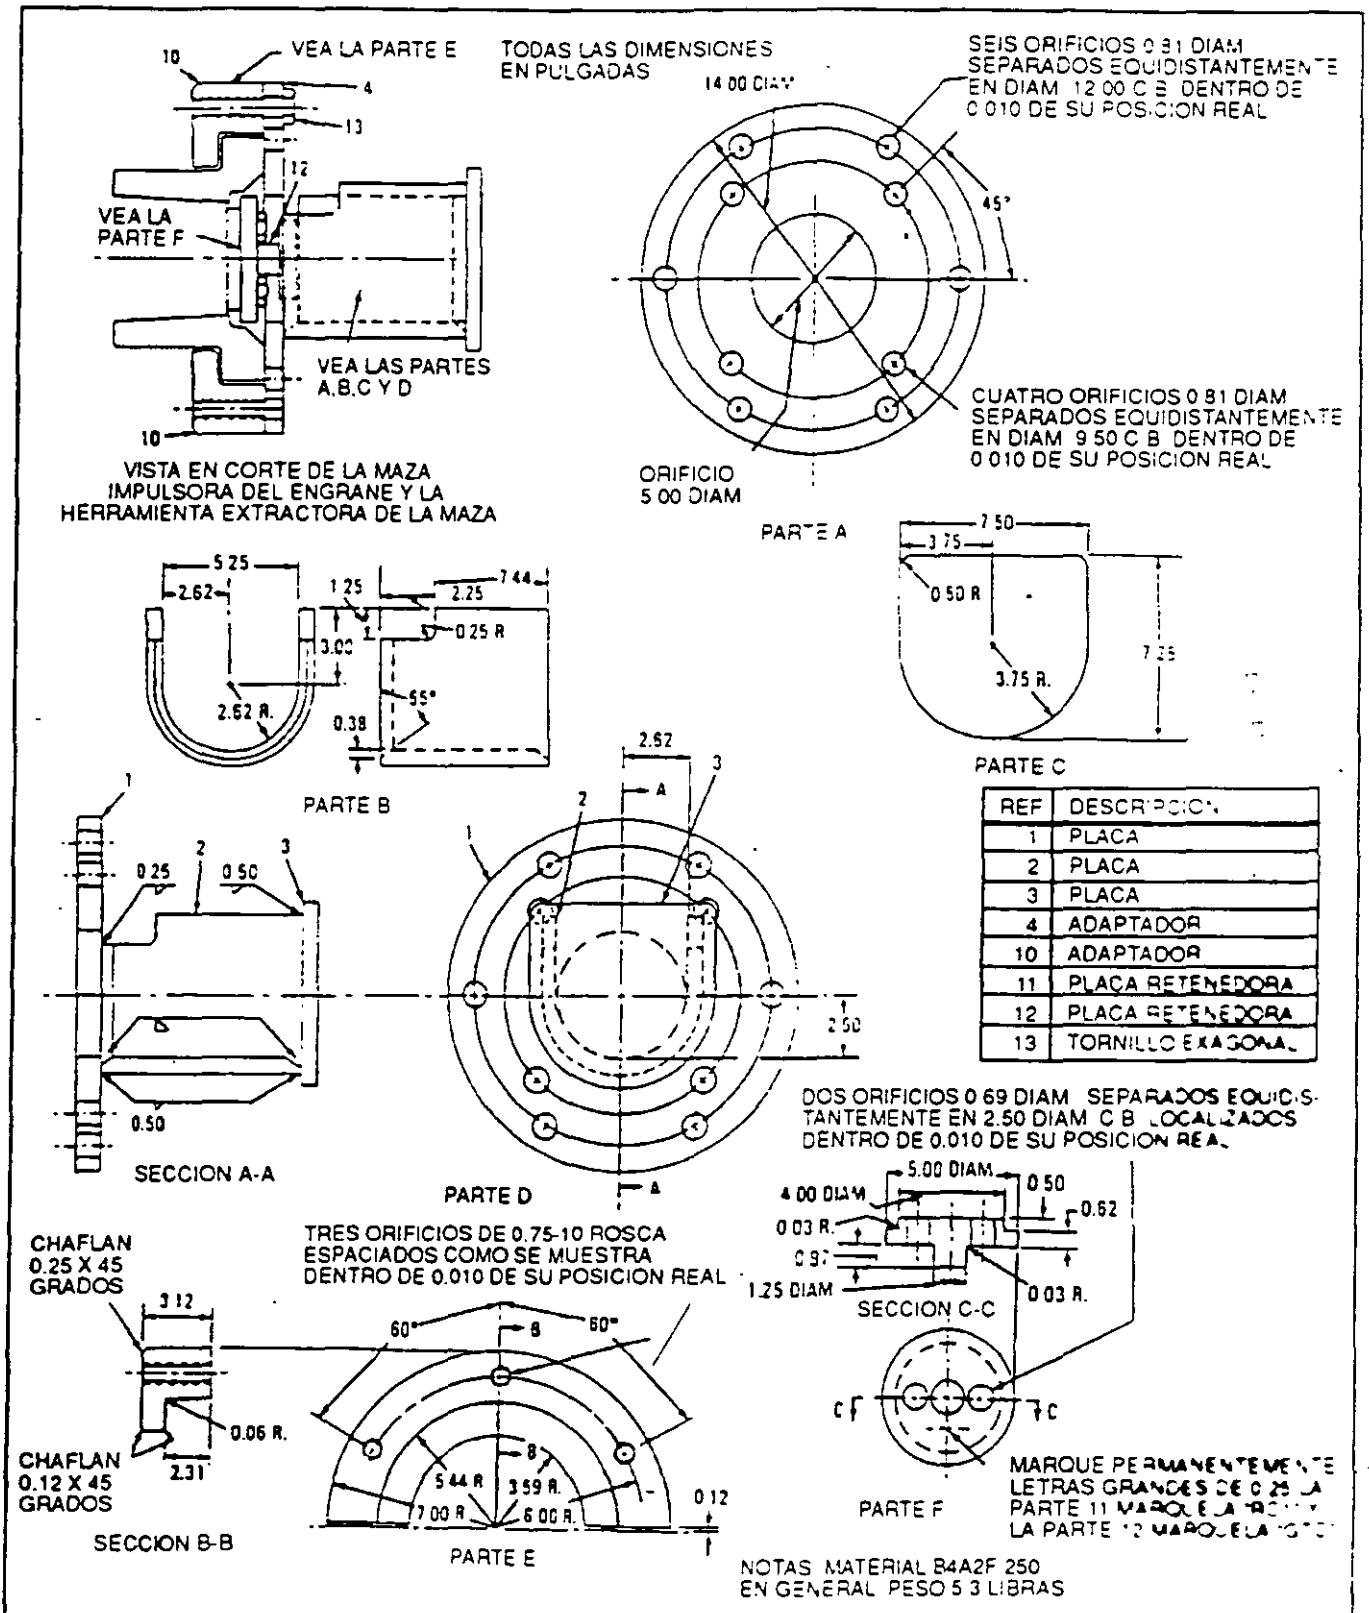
HERRAMIENTAS PARA REMOCION DE LA MAZA DEL COPLER ENGRANADO E 32862 S
